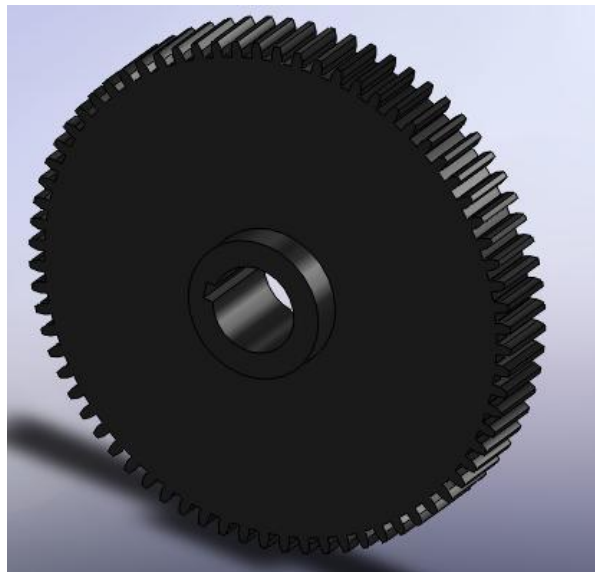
72-зубчаста циліндрична шестерня
